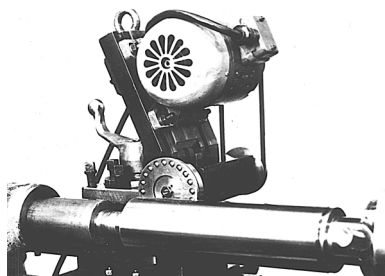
Вибронакатывание цилиндрической поверхности штоков на токарно-винторезном станке с помощью ротационной многошаровой головки
